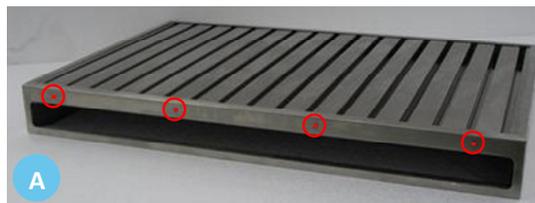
Installation des vis de la dalle Unifloor du kit de CV
